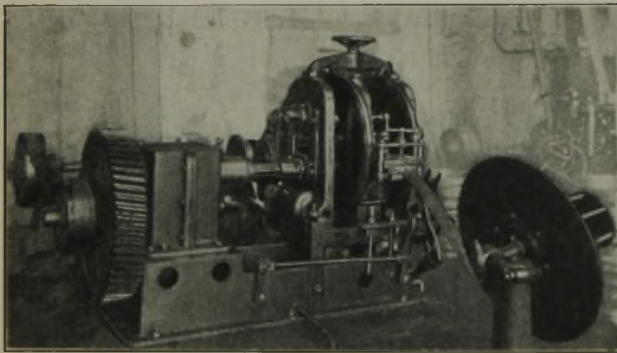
Kaltwalzgerüst mit Tragringen.
